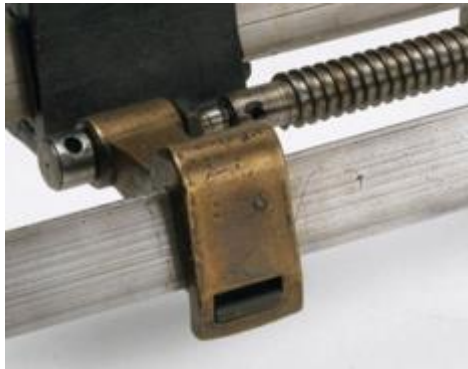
Detalle del sistema de engranajes del torno de Henry Maudslay, 1800. Imagen recortada [60].
